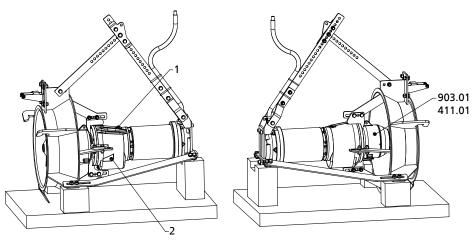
Llenado del líquido lubricante; Amaline 500, 600, 800
